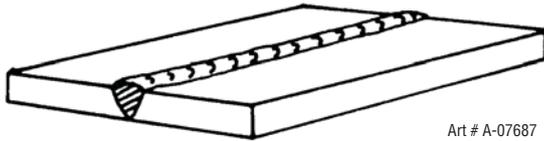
Position à plat, soudure par aboutement à l'horizontale
